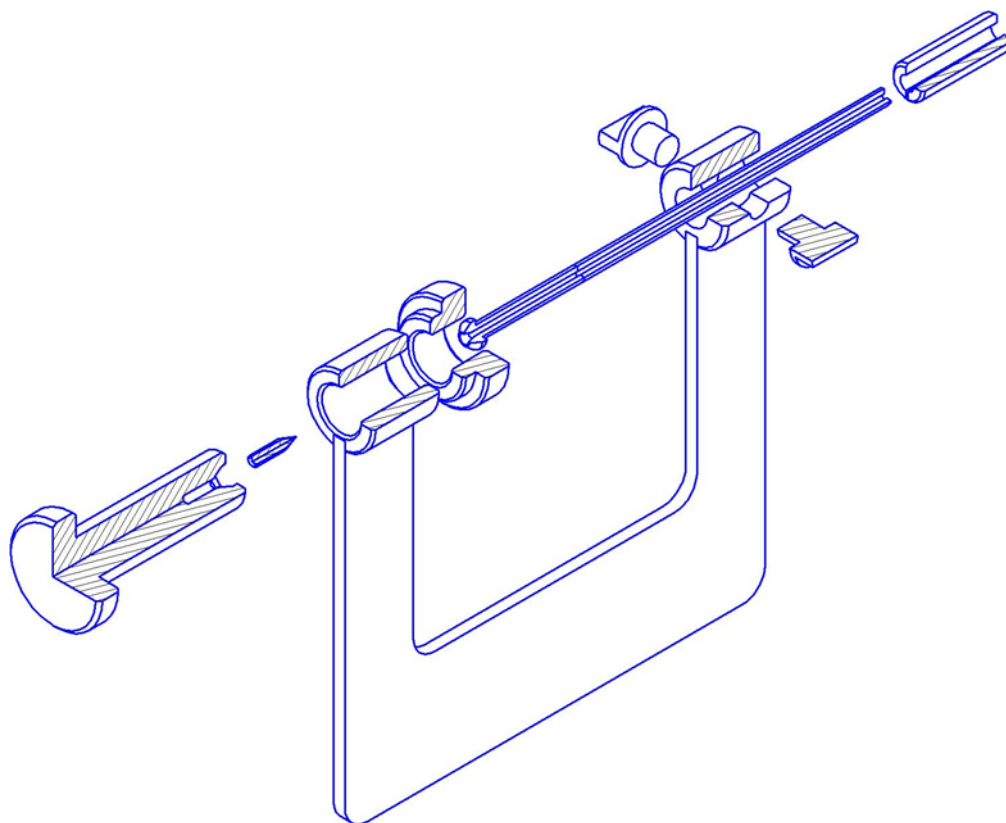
Приспособление для приварки наконечника топливопроводов высокого давления с разнесенными деталями
